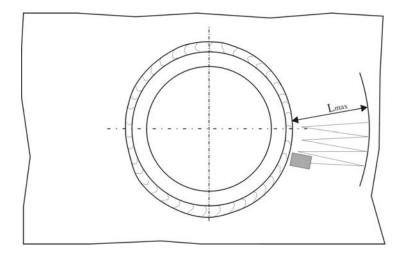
Схема сканирования углового сварного шва приварки люка-лаза к стенке PBC.
